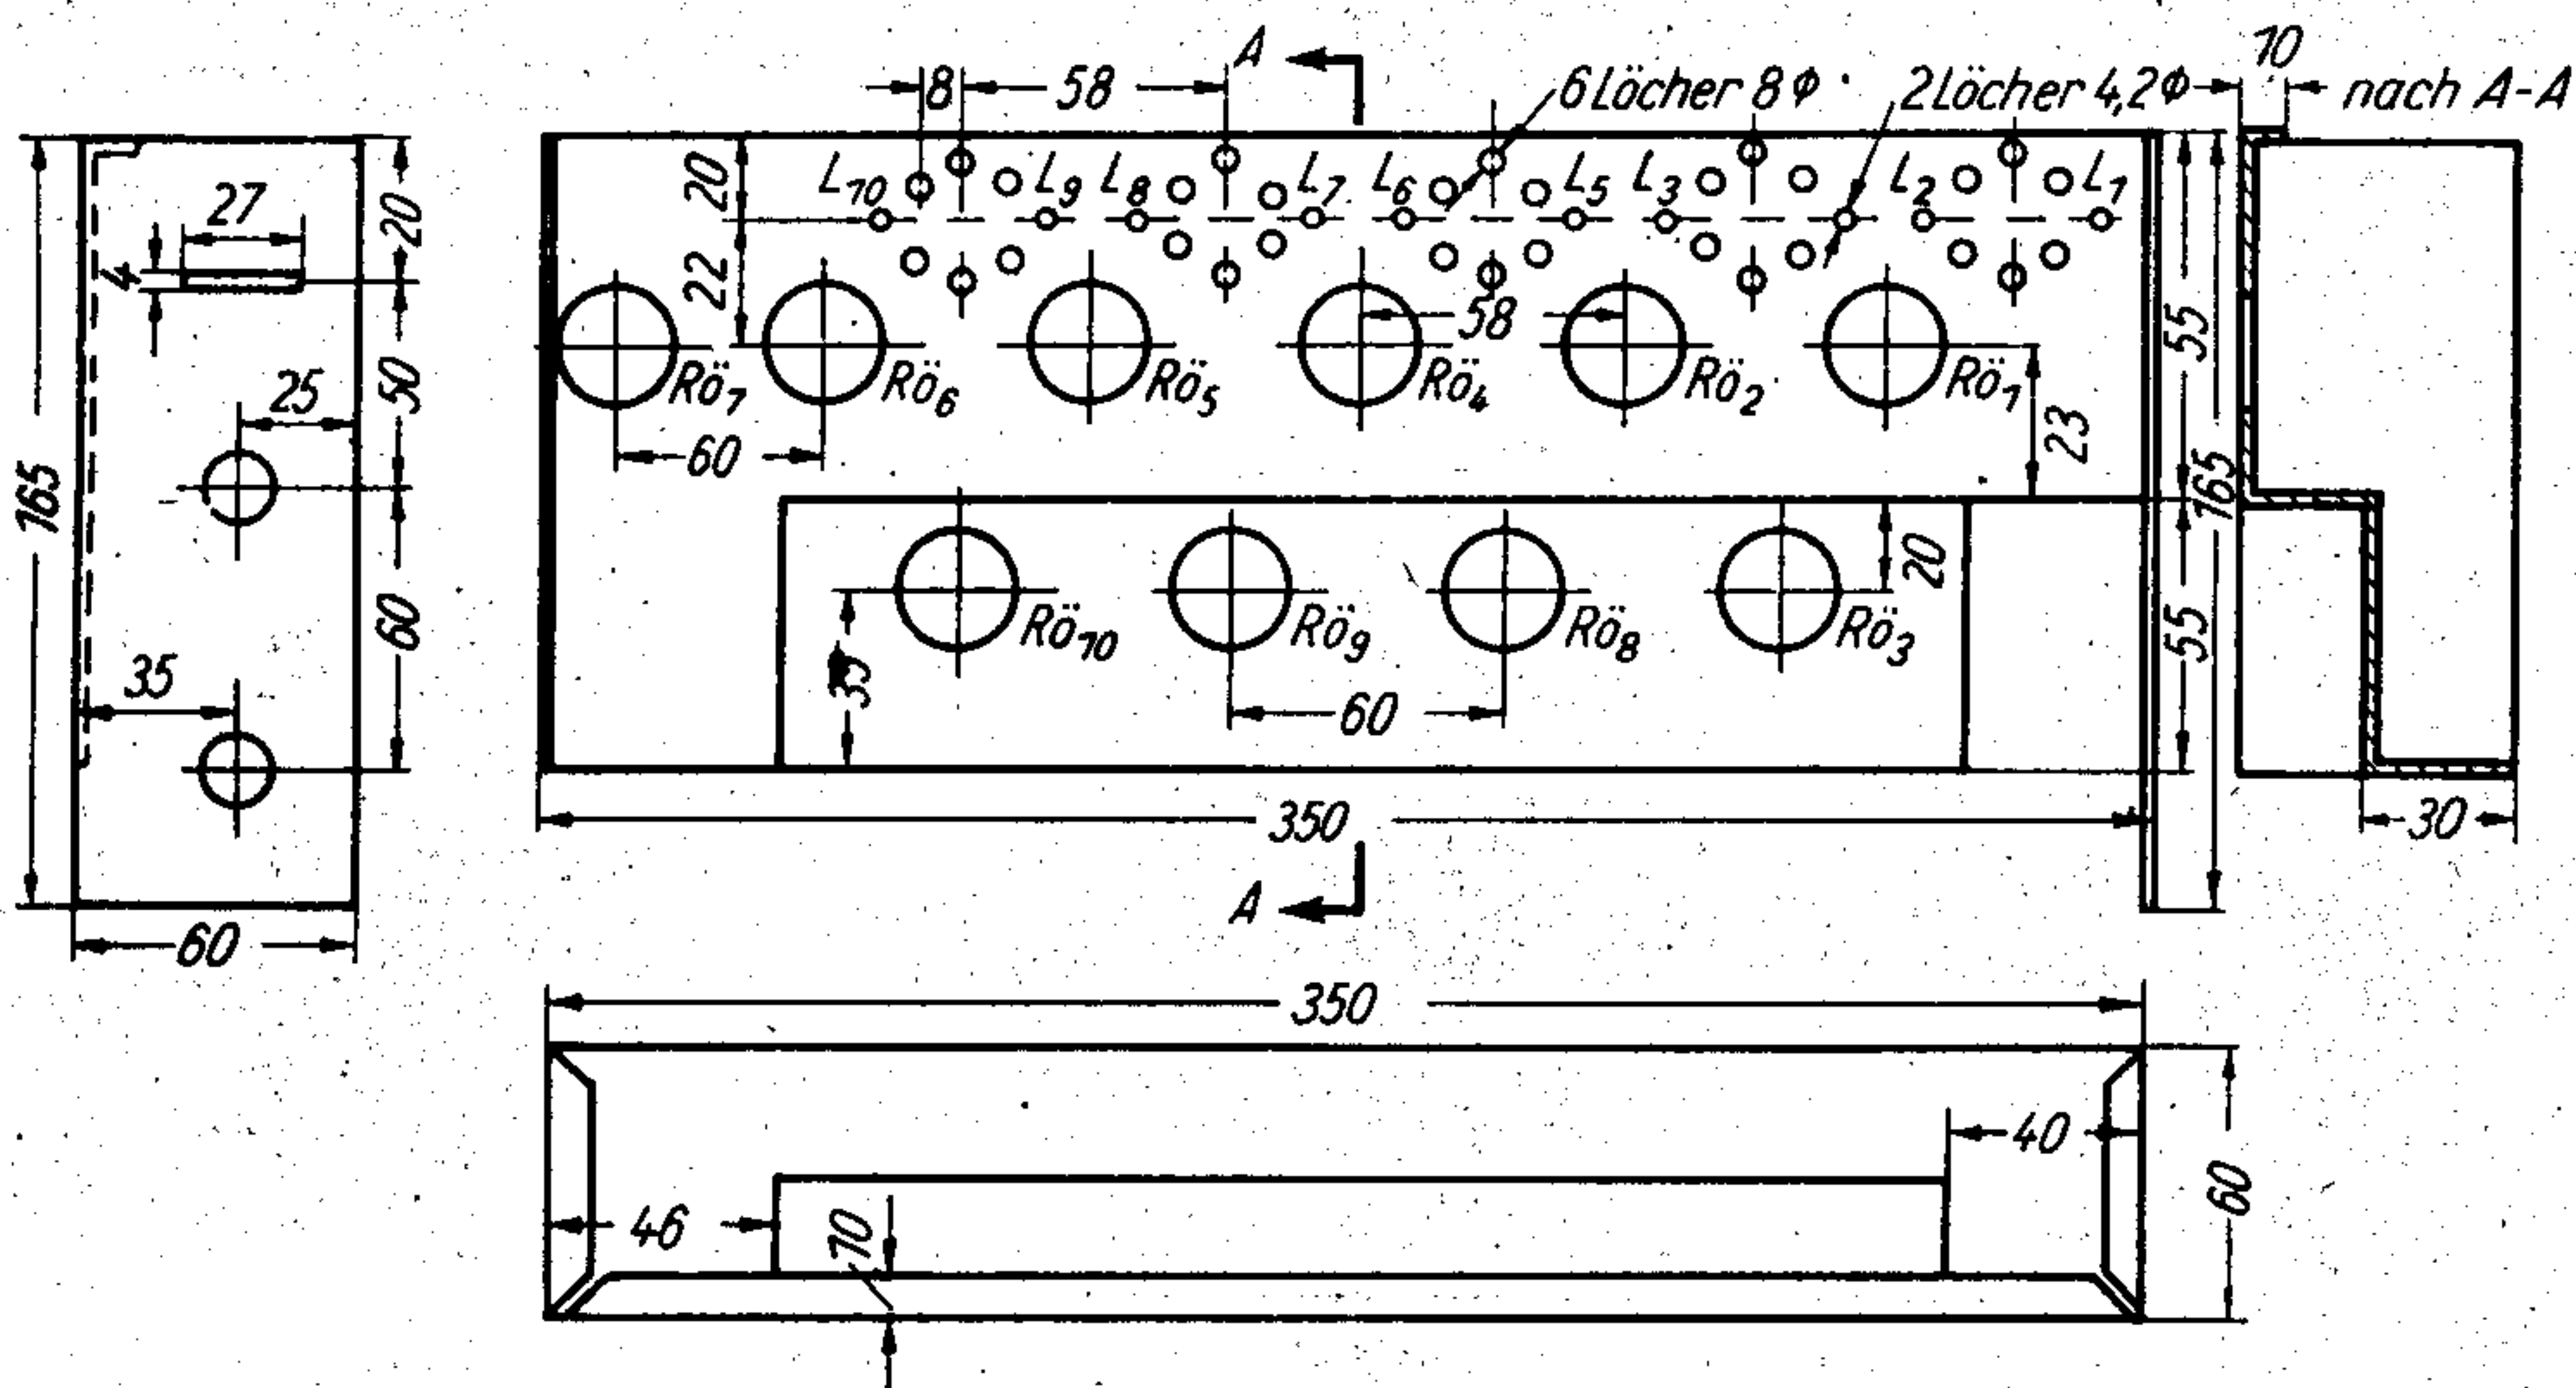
Einteilung des Chassis für den Bild- und den Tonempfänger
